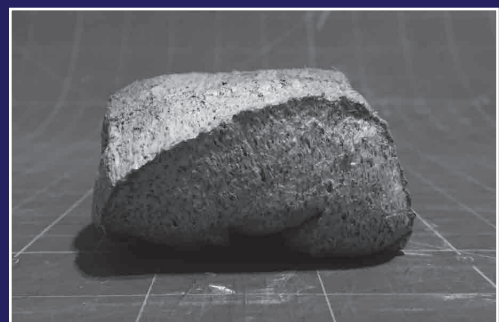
Deformación generada al inicio de la extrusión de una pieza.
